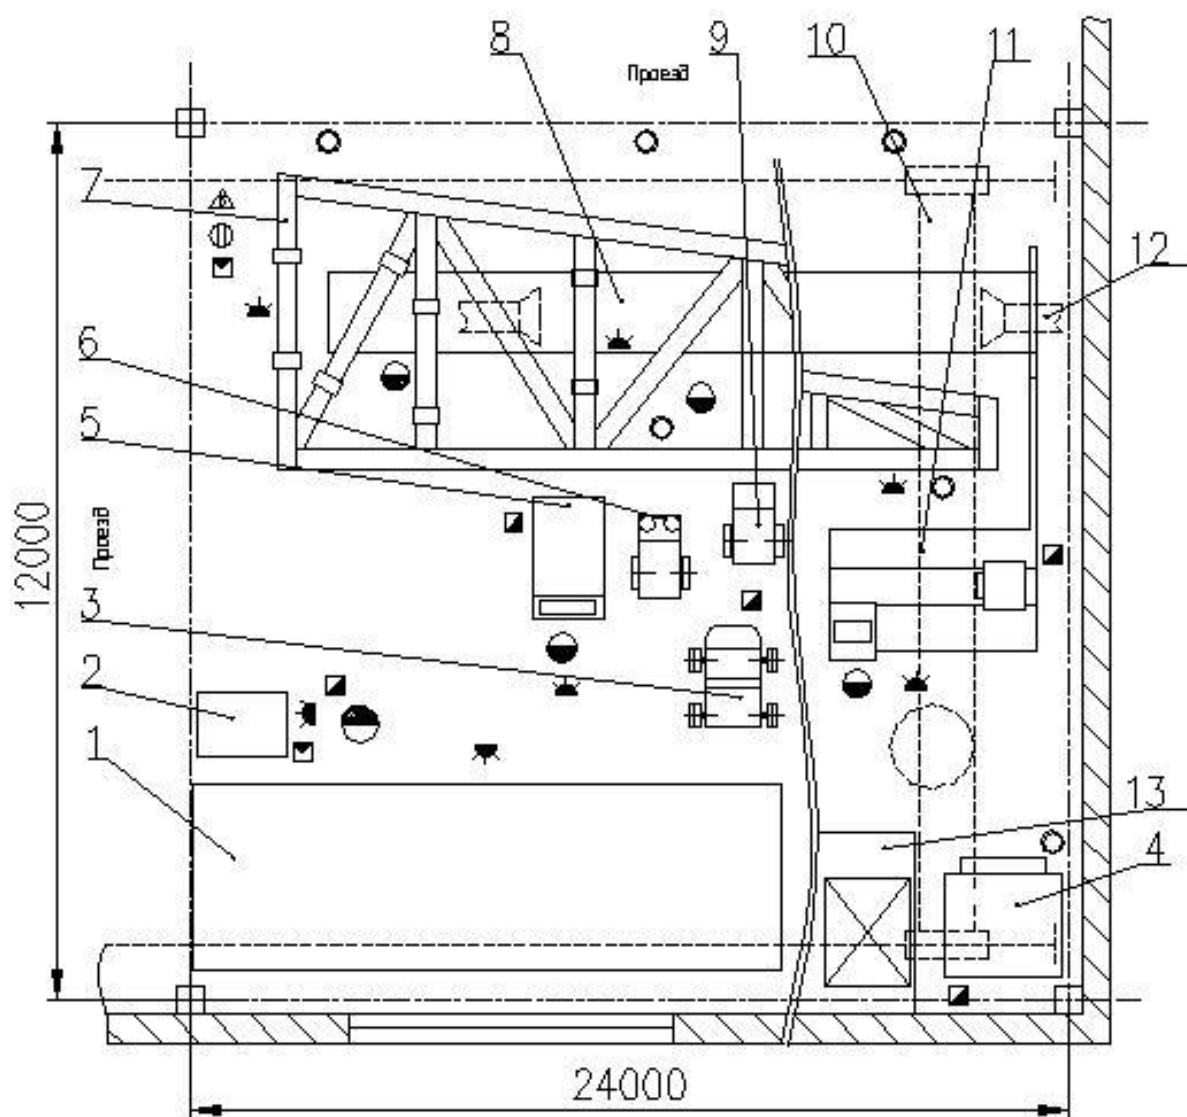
Компоновочная схема участка сварки ферм
